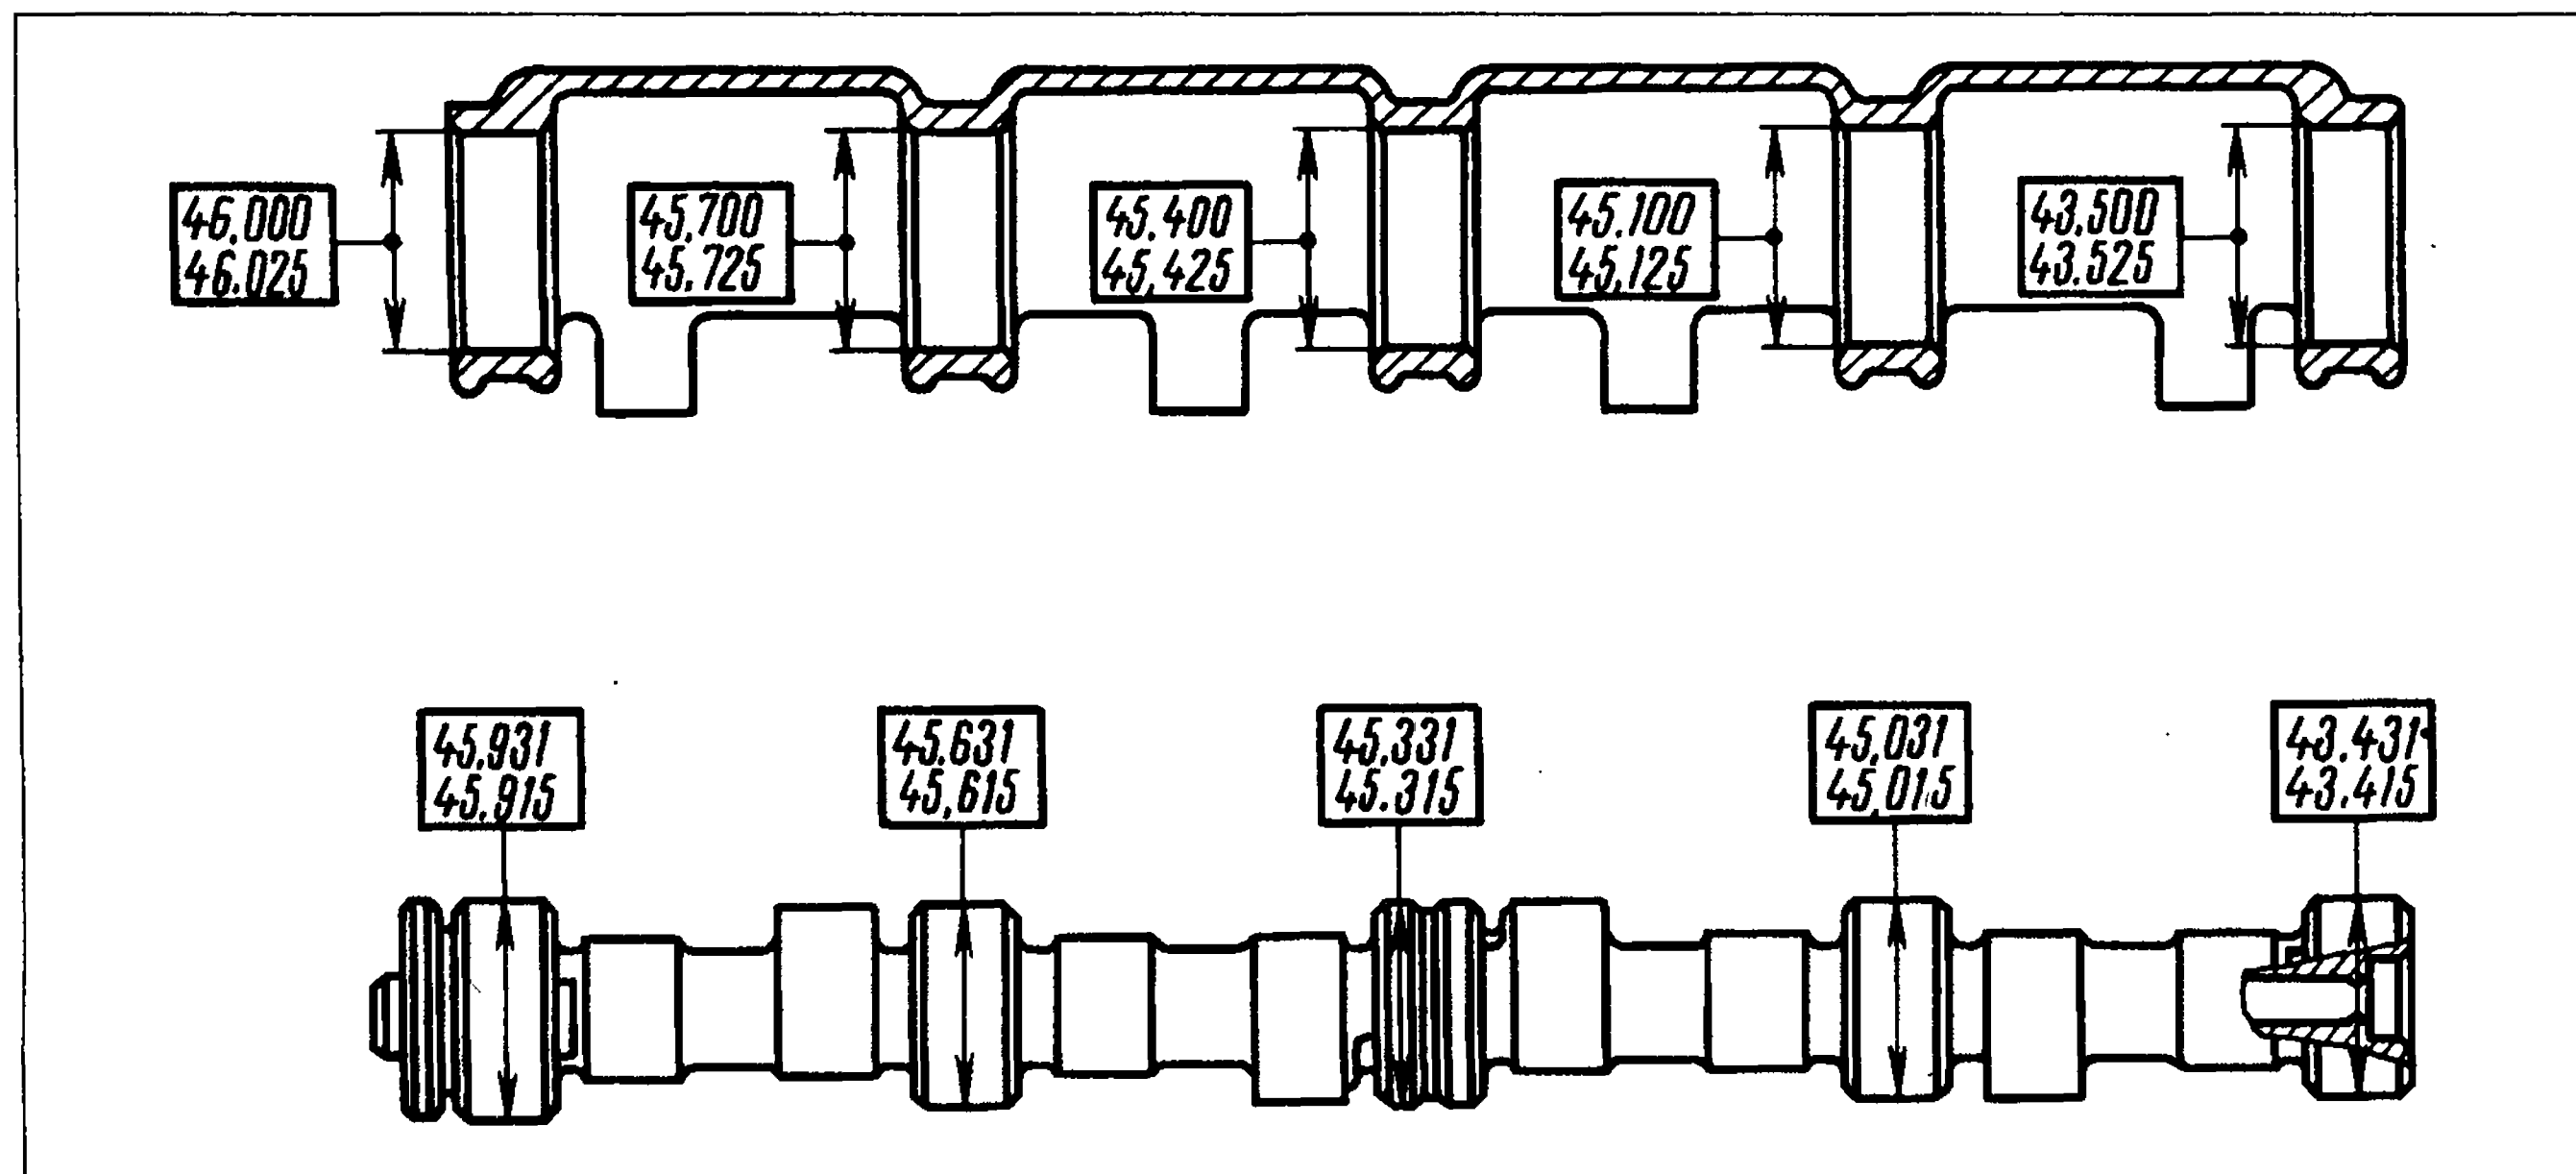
Основные размеры распределительного вала и расточек в корпусе подшипников распределительного вала
